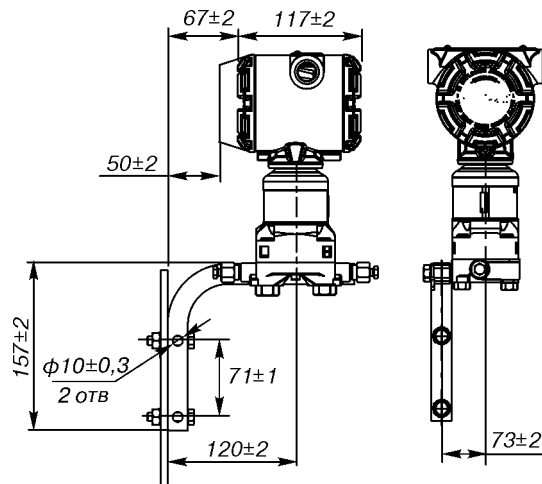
Монтаж на панели (стене) расходомеров типа SFA.
